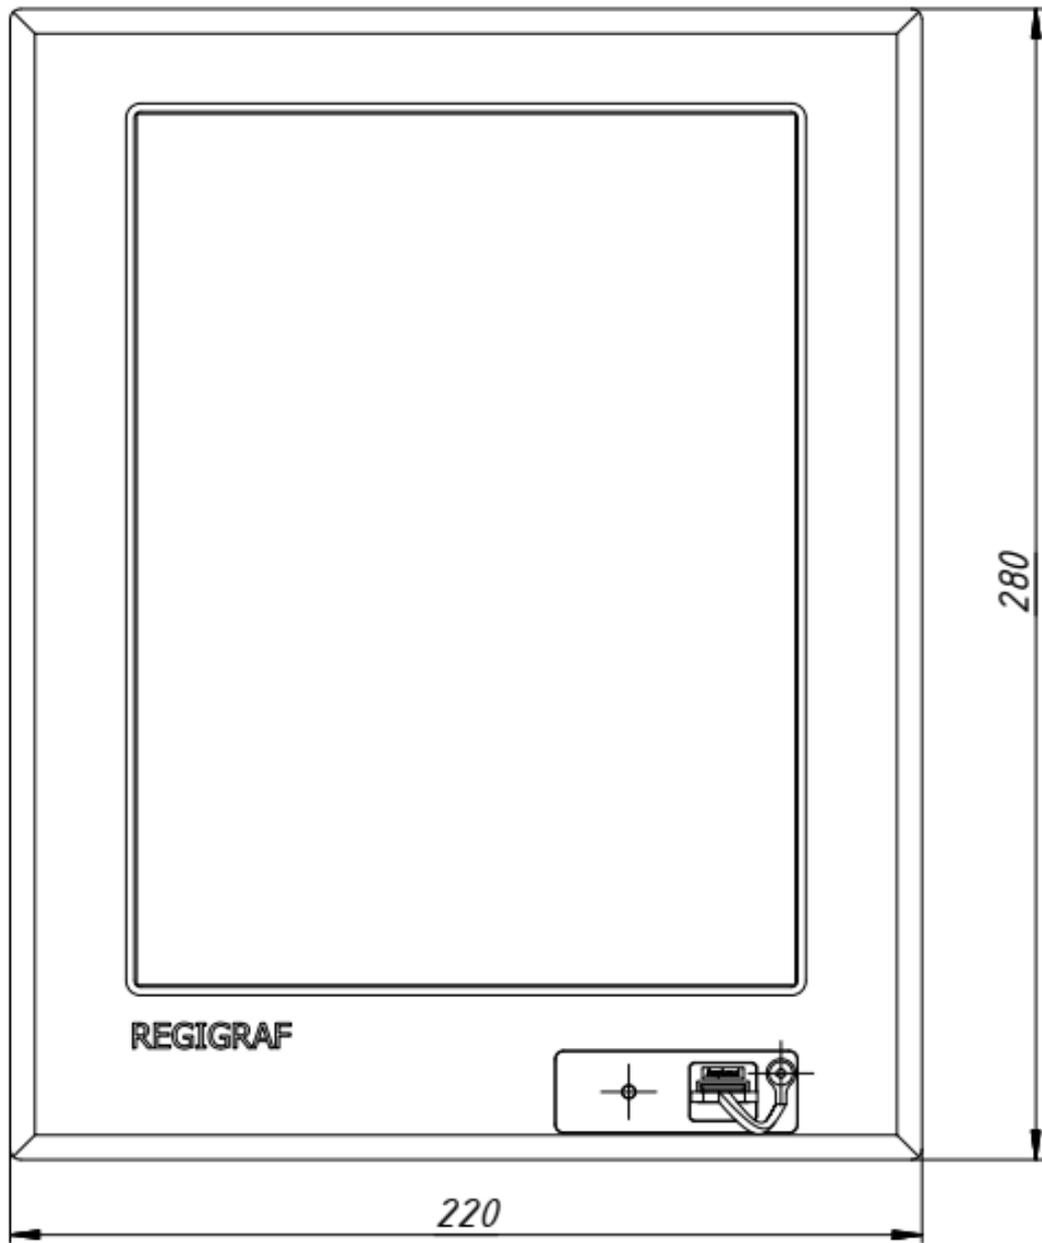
Габаритный чертёж прибора в исполнении Ф1772–4, вид спереди
